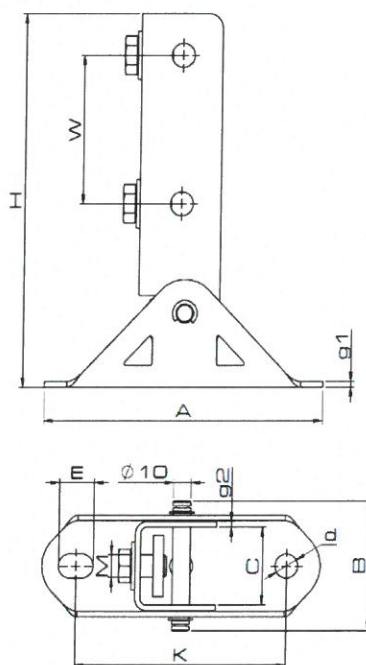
Kształtki montażowe do odciągów DCL-M12/16
